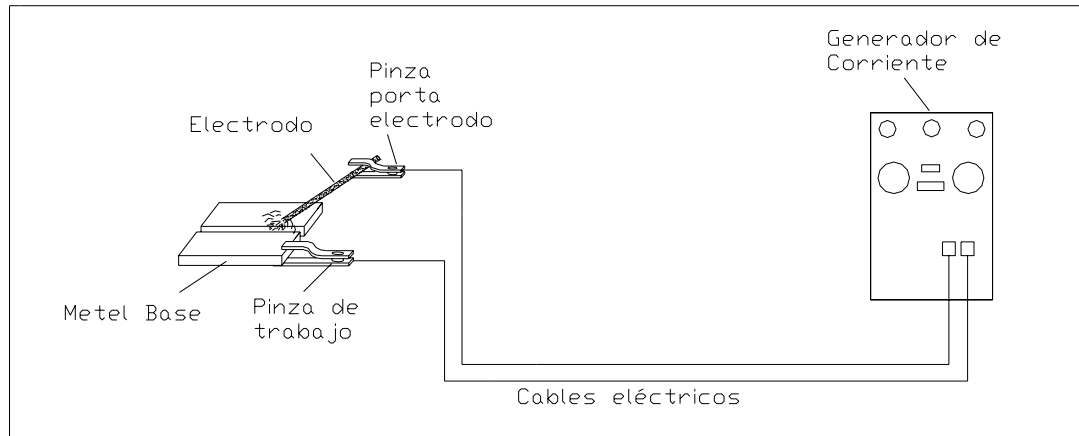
EQUIPO DE SOLDADURA SMAW.
